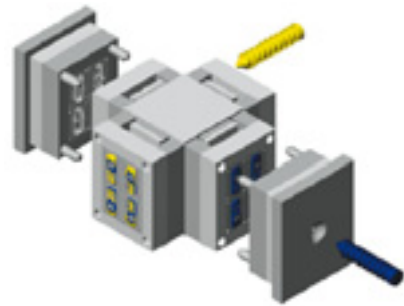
Prinzipieller Aufbau eines Werkzeugs für die Etagenwend- oder Würfeltechnik [13.14]
